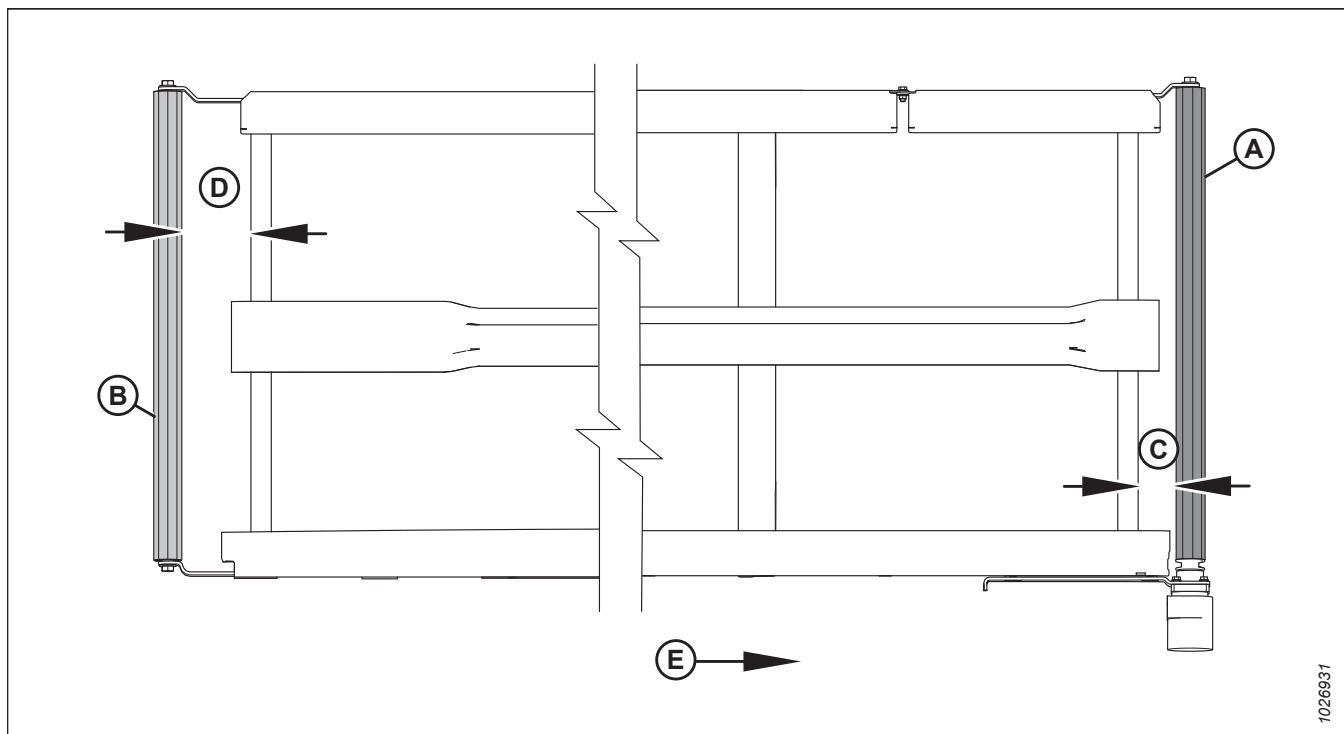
Vue d'ensemble de l'alignement du tapis
